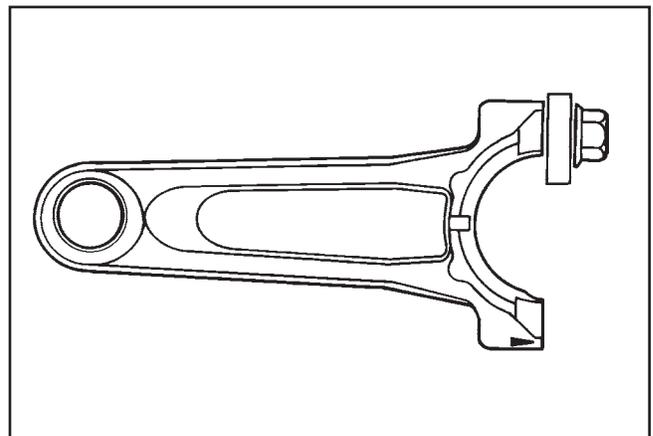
Ferramenta para Braço Oscilante/Cambota.
